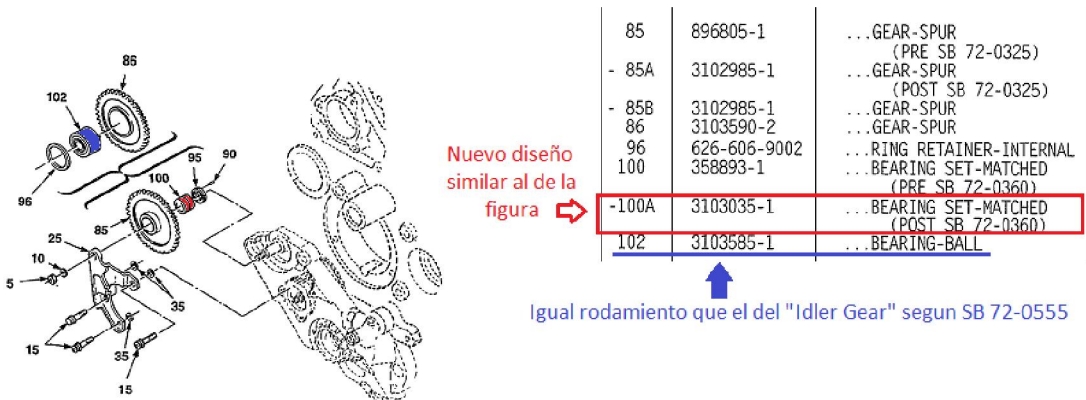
Ensamblaje de Generador de taquímetro y sensor de torque posterior a la aplicación del SB 72-0232 (resaltado en rojo, sobre el dibujo, la primer versión del rodamiento en cuestión; recuadrado en rojo sobre la tabla la versión posterior al SB 72-0360; y en azul, la última versión del rodamiento según SB 72-0555).
